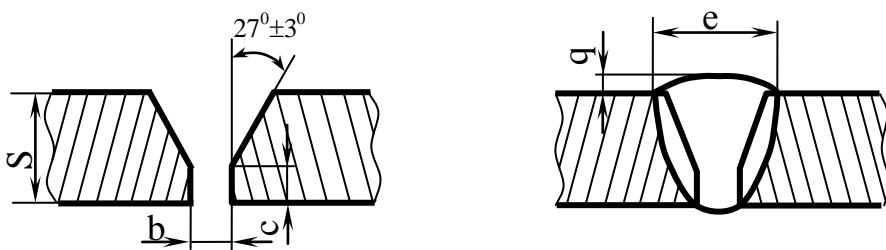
Сварное соединение до и после сварки
